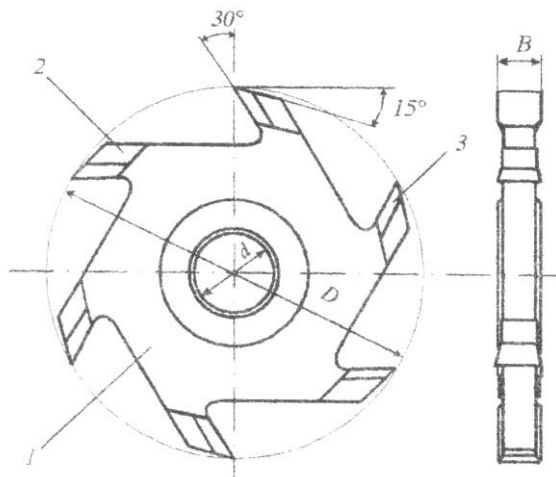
Конструкція пазової фрези типу 1 для фрезерування вздовж волокон
